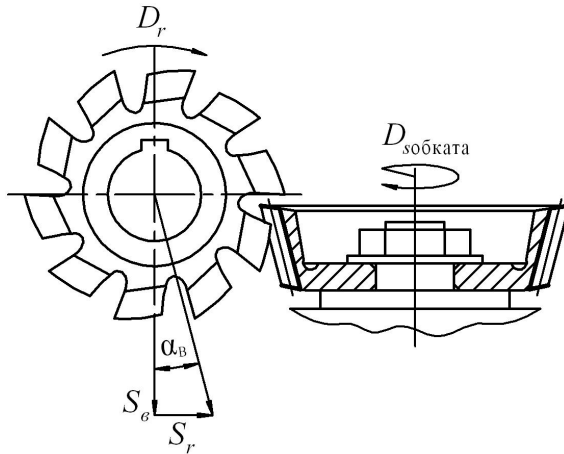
Фрезерование зубьев на заготовке долбяка
